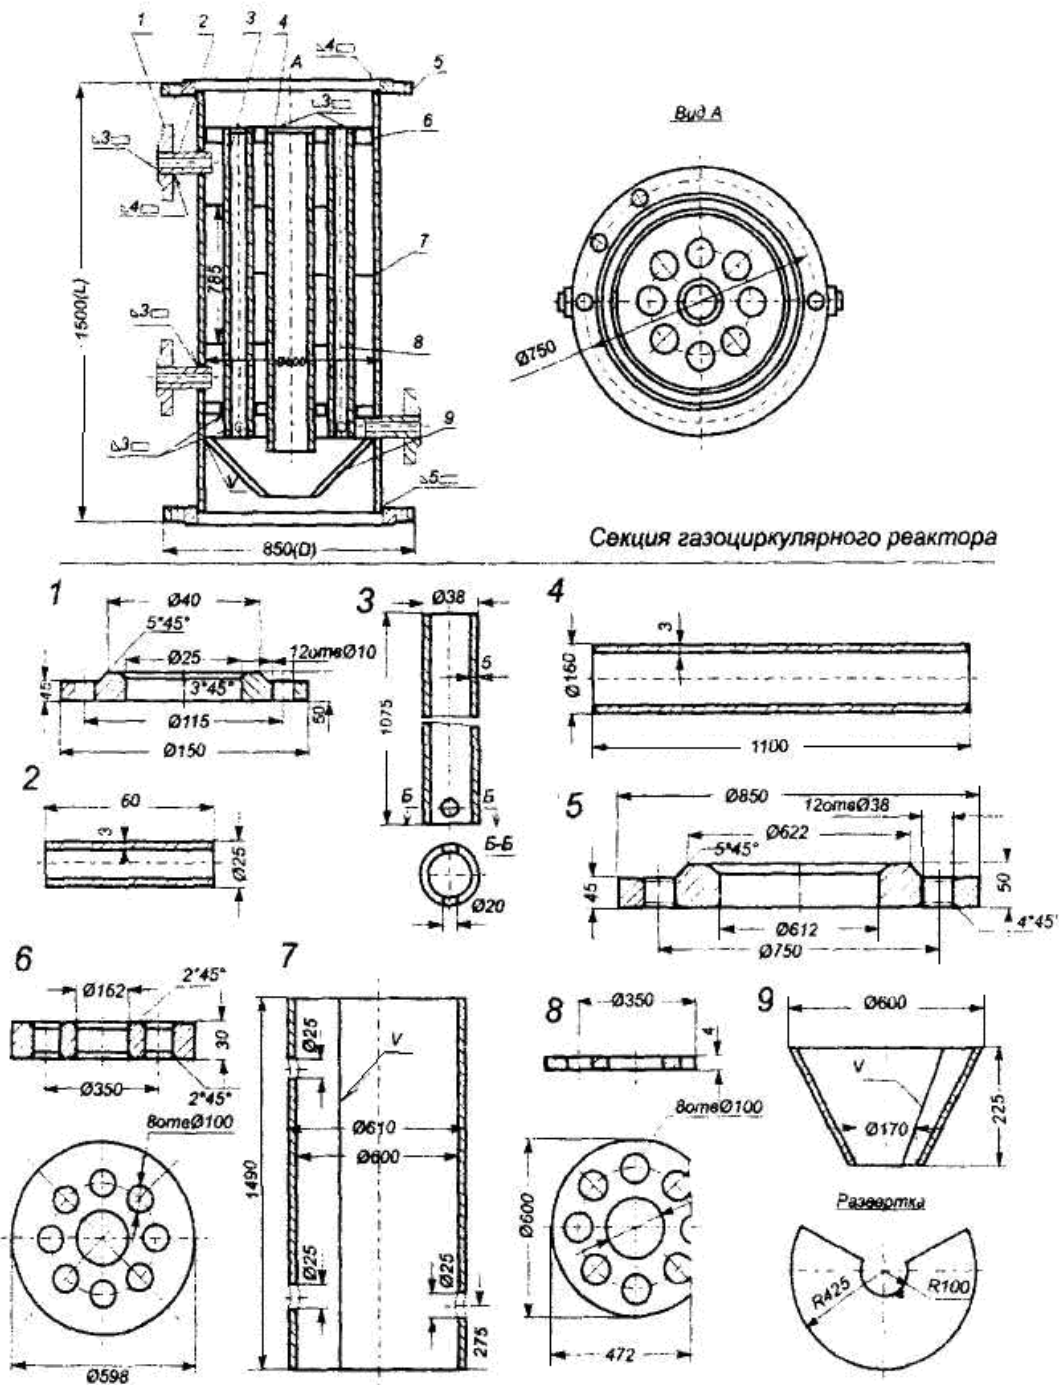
Схема газоциркулярного реактора и его детализовки для задания № 3
